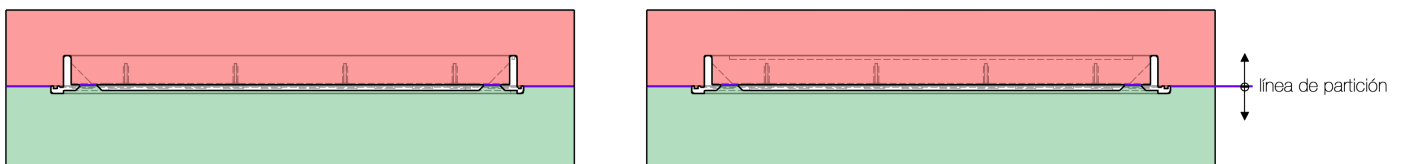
mitades molde pieza "1.3.- Estructura cubierta superior"
